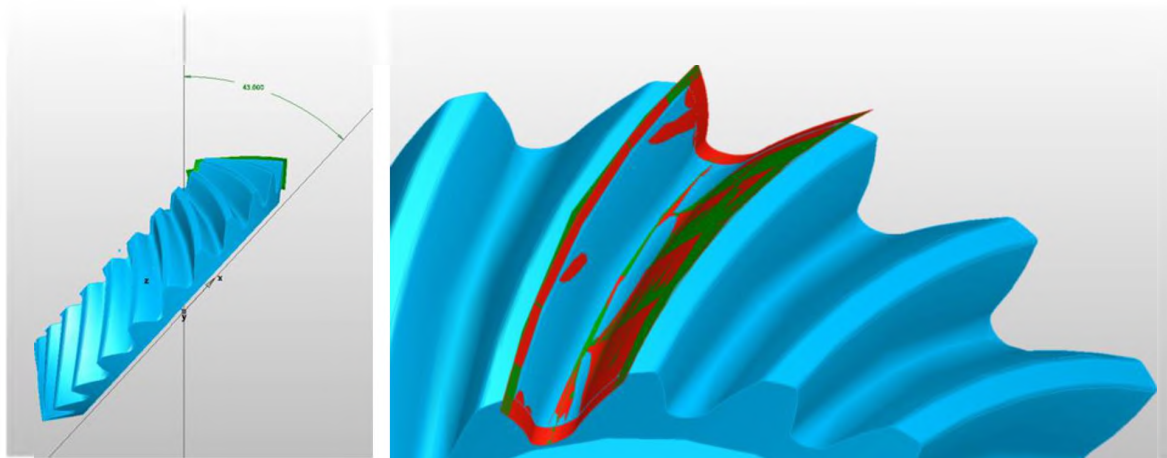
Кут обробки деталі та вибір поверхні
